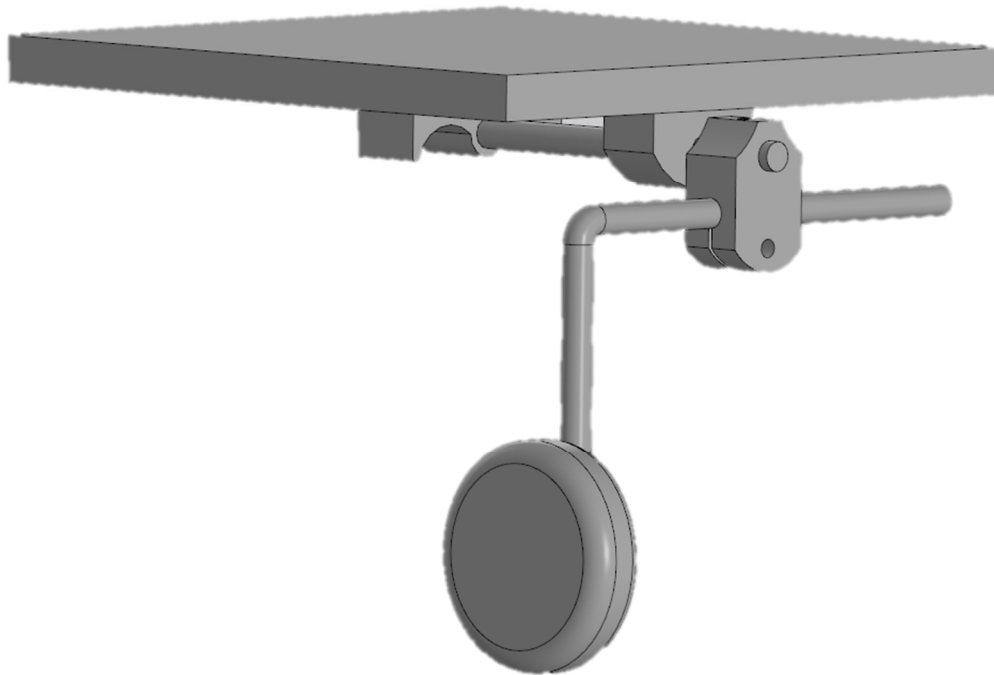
Тривимірний збірний механізм притискання лапки швейної машини
